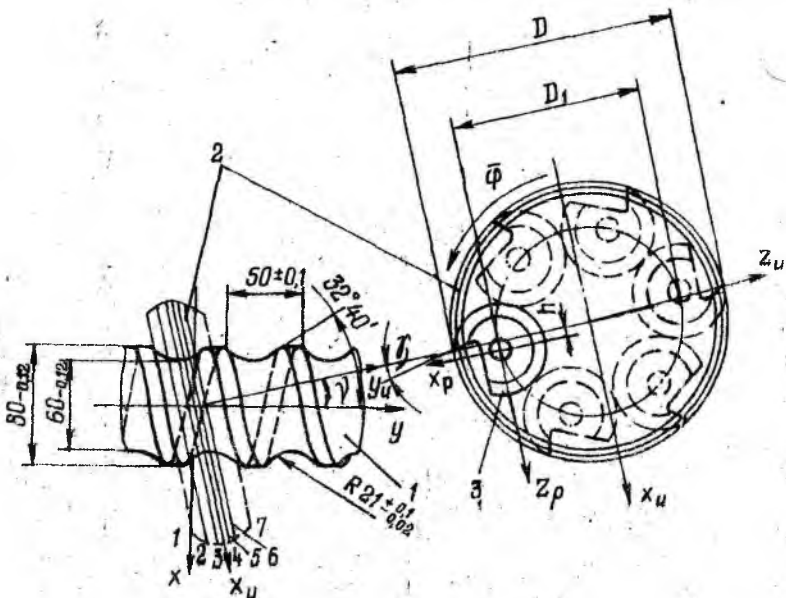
Фасонная фреза для обработки винтовой поверхности:
